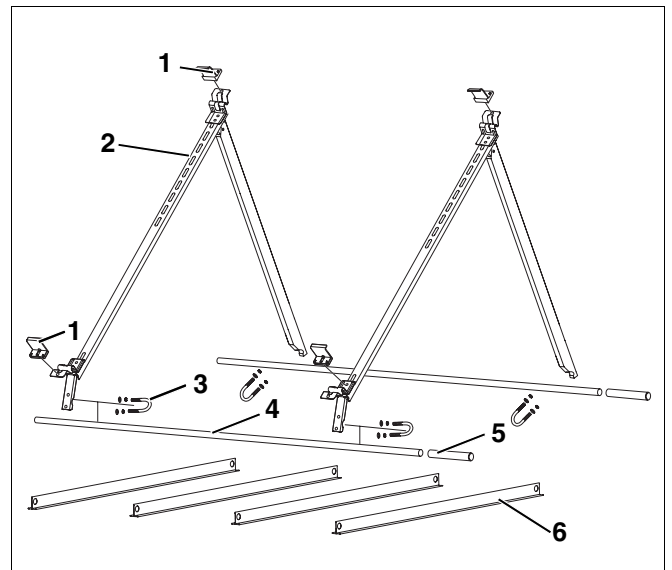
Juego de montaje para tejado plano, p. ej. juego horizontal
